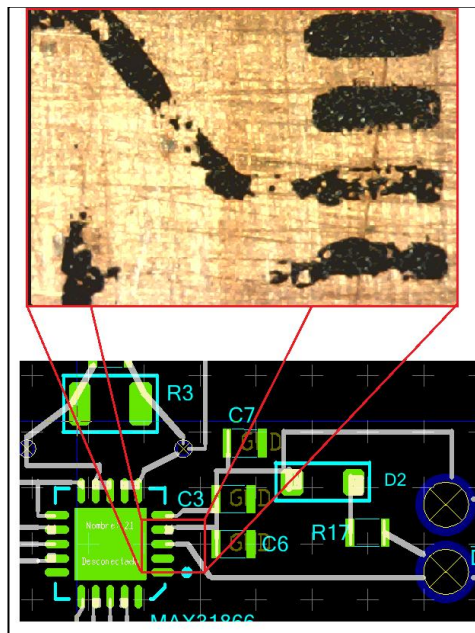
Acercamiento defectos presentados en la transferencia al PCB.
